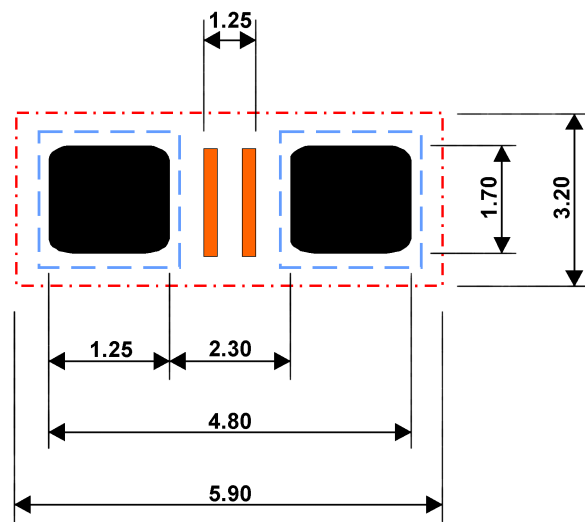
Widerstand - Dimensionen SMD 1206, Quelle: http://www.siongboon.com/projects/2005-09-07_home_pcb_fabrication/footprint/1206.gif
